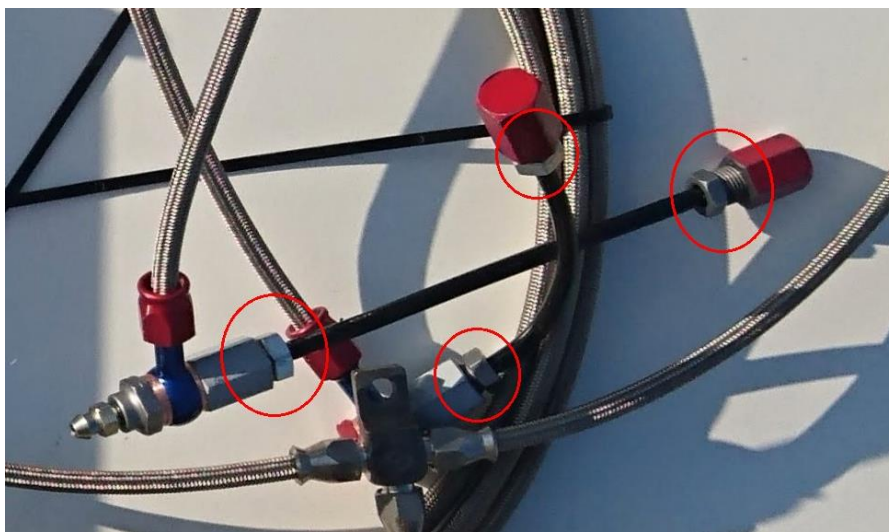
Brzdové zařízení s ruční hydraulickou pumpou během zkušebního testu
